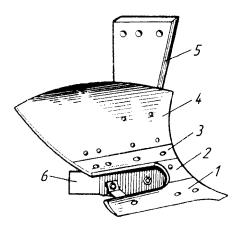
Вид корпуса с тремя лемехами (вырезной): 1, 2, 3 — нижний, боковой и верхний лемеха; 4 — отвал; 5 — стойка; 6 — полевая доска
